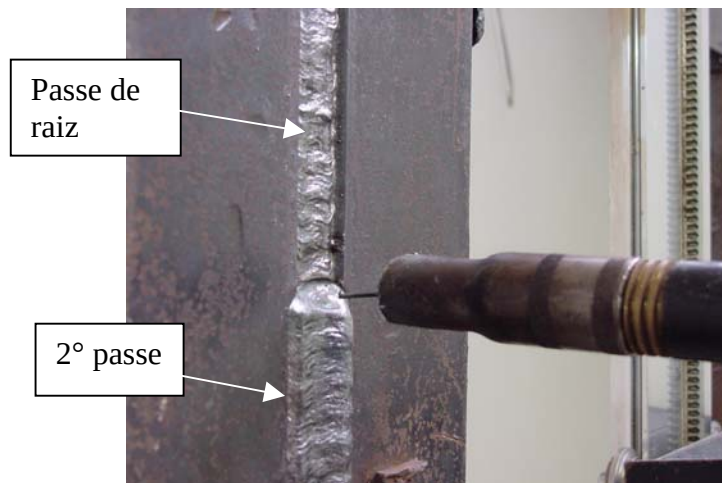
Corpo de prova soldado dentro do Labsolda.
